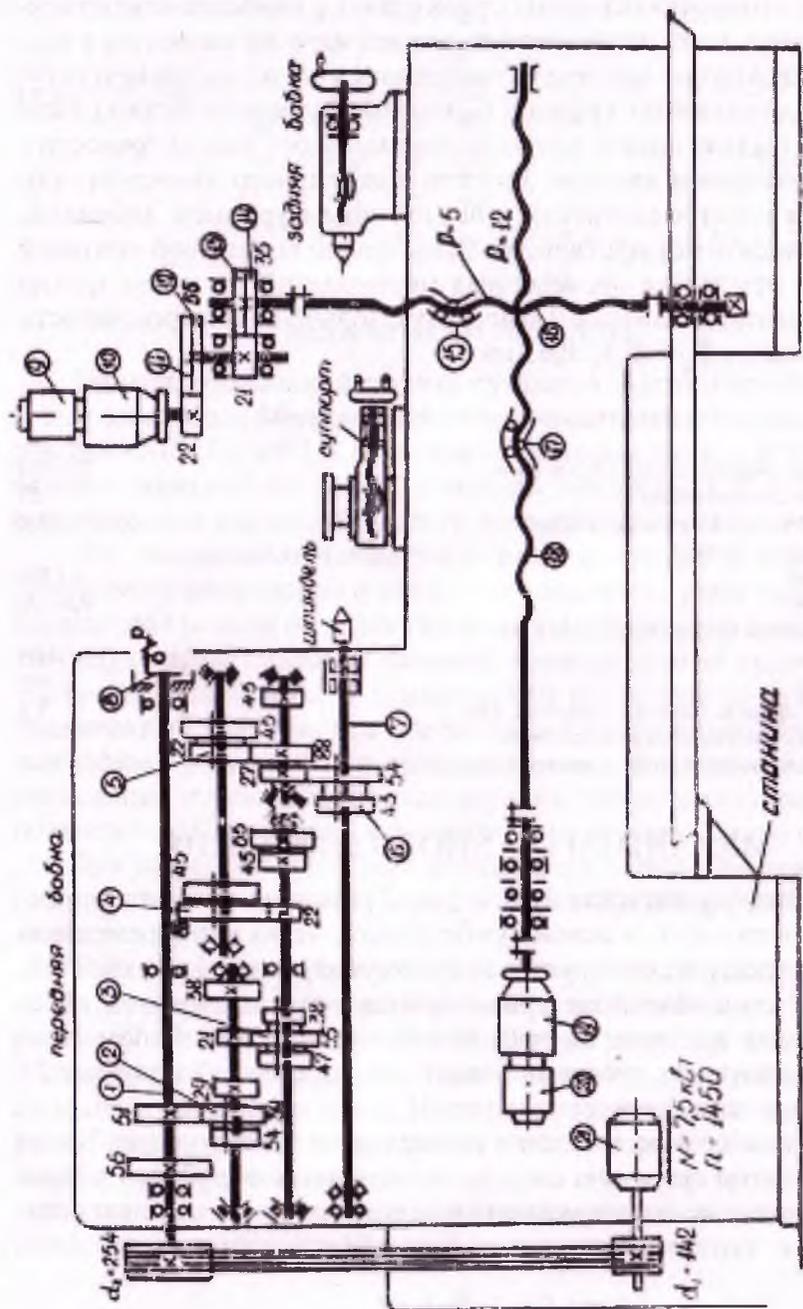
Кинематическая схема и основные узлы станка К62ФЗС1
